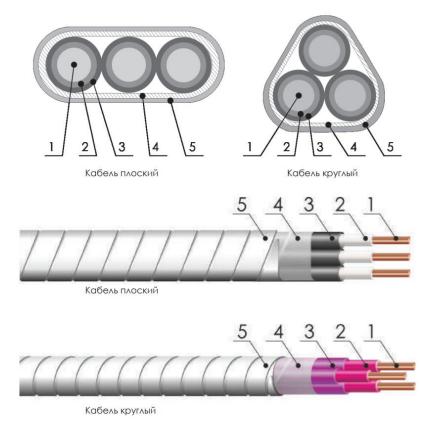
Схематичные чертежи поперечного сечения кабелей и внешний вид конструктивных элементов:
